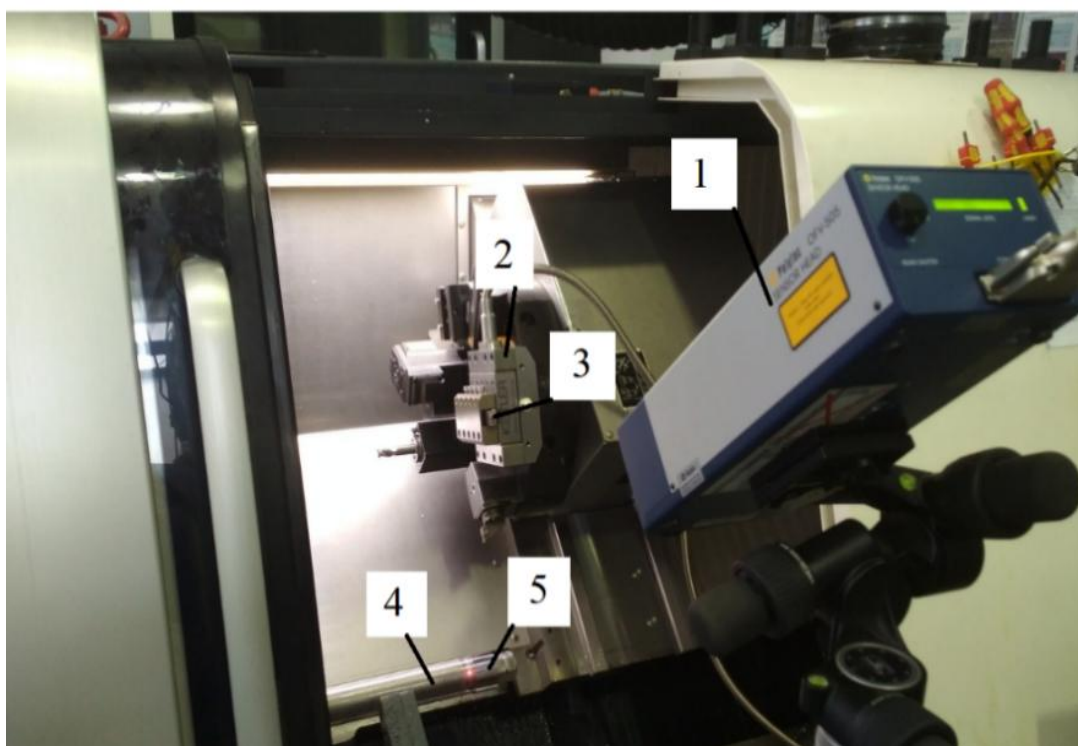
Экспериментальная установка: 1 - лазерный виброметр Polytec OFV-505; 2 - динамометр Kistler Type 9129AA; 3 – закрепленный инструмент; 4 – заготовка, закрепленная в трехкулачковом патроне; 5 – лазерная фокусировка, установленная на заготовке.
